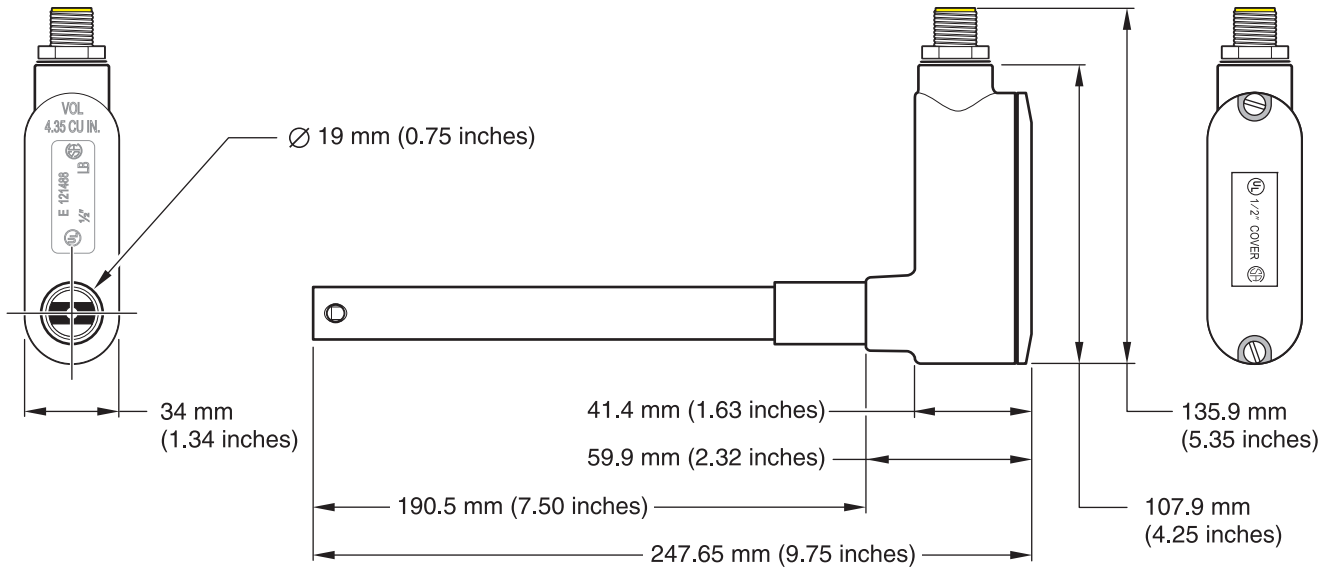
Drukdichte sensor, 0,75 duim diameter
